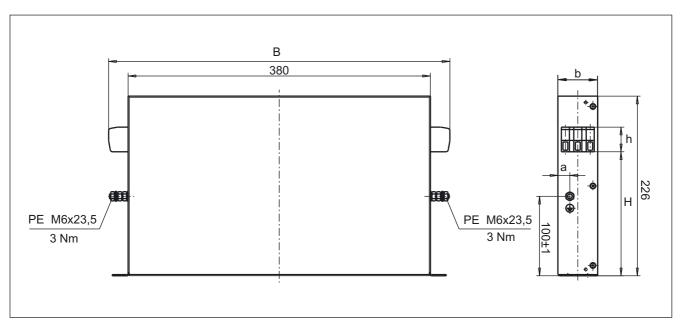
Disegno quotato del filtro di rete per gli Smart Line Module 16 kW e 36 kW
